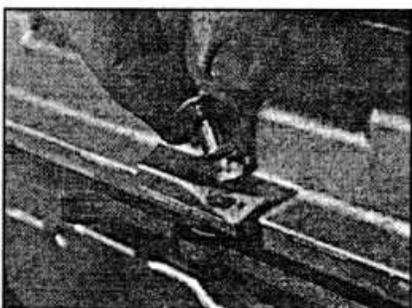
С.6. Резиновые прокладки должны быть установлены под каждый болт крепления крышки головки.
